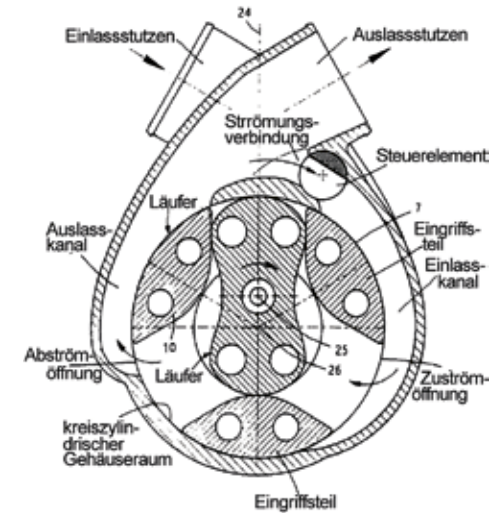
Konstruktionszeichnung von Franz Obrist für eine „innenachsige Drehkolbenmaschine“, 1993
